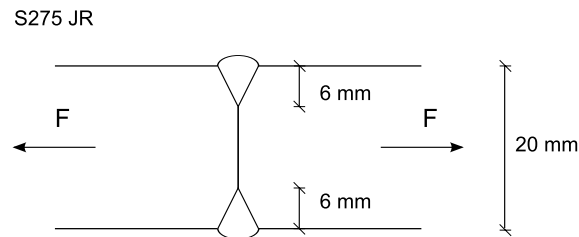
Soldadura de topo com penetração parcial
